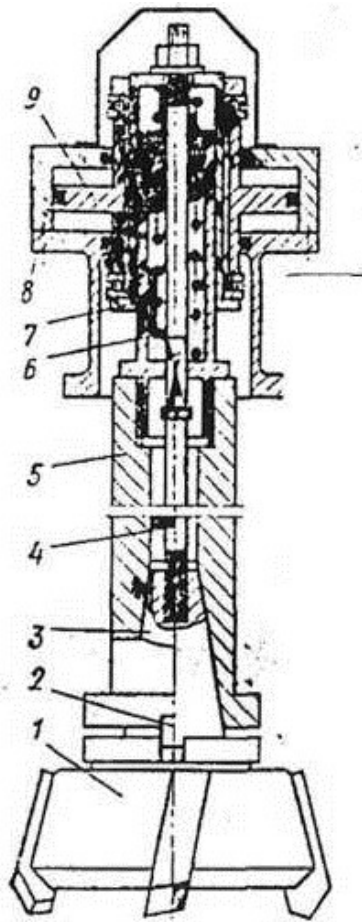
12. Закріплення фрез з оправкою в шпинделі вертикально-фрезерного верстата
